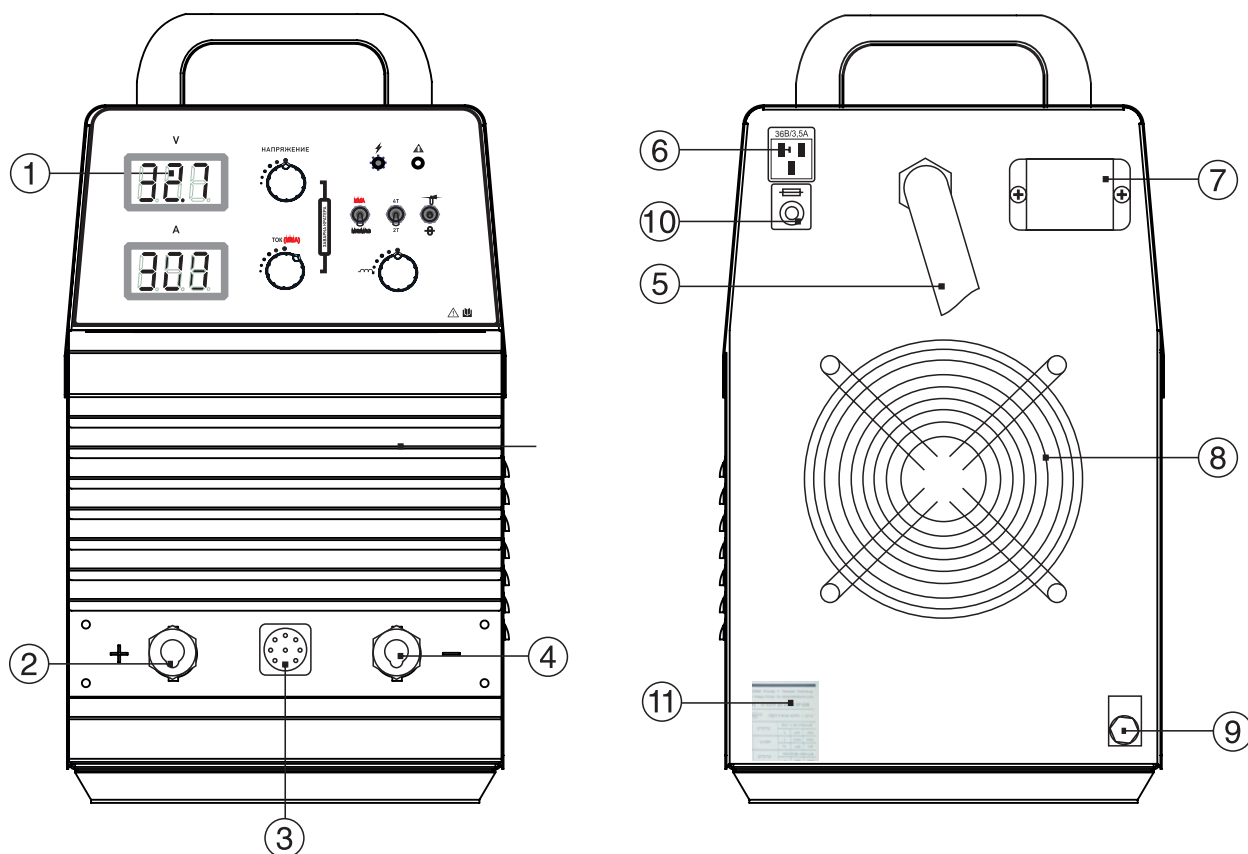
Внешний вид сварочного аппарата.
